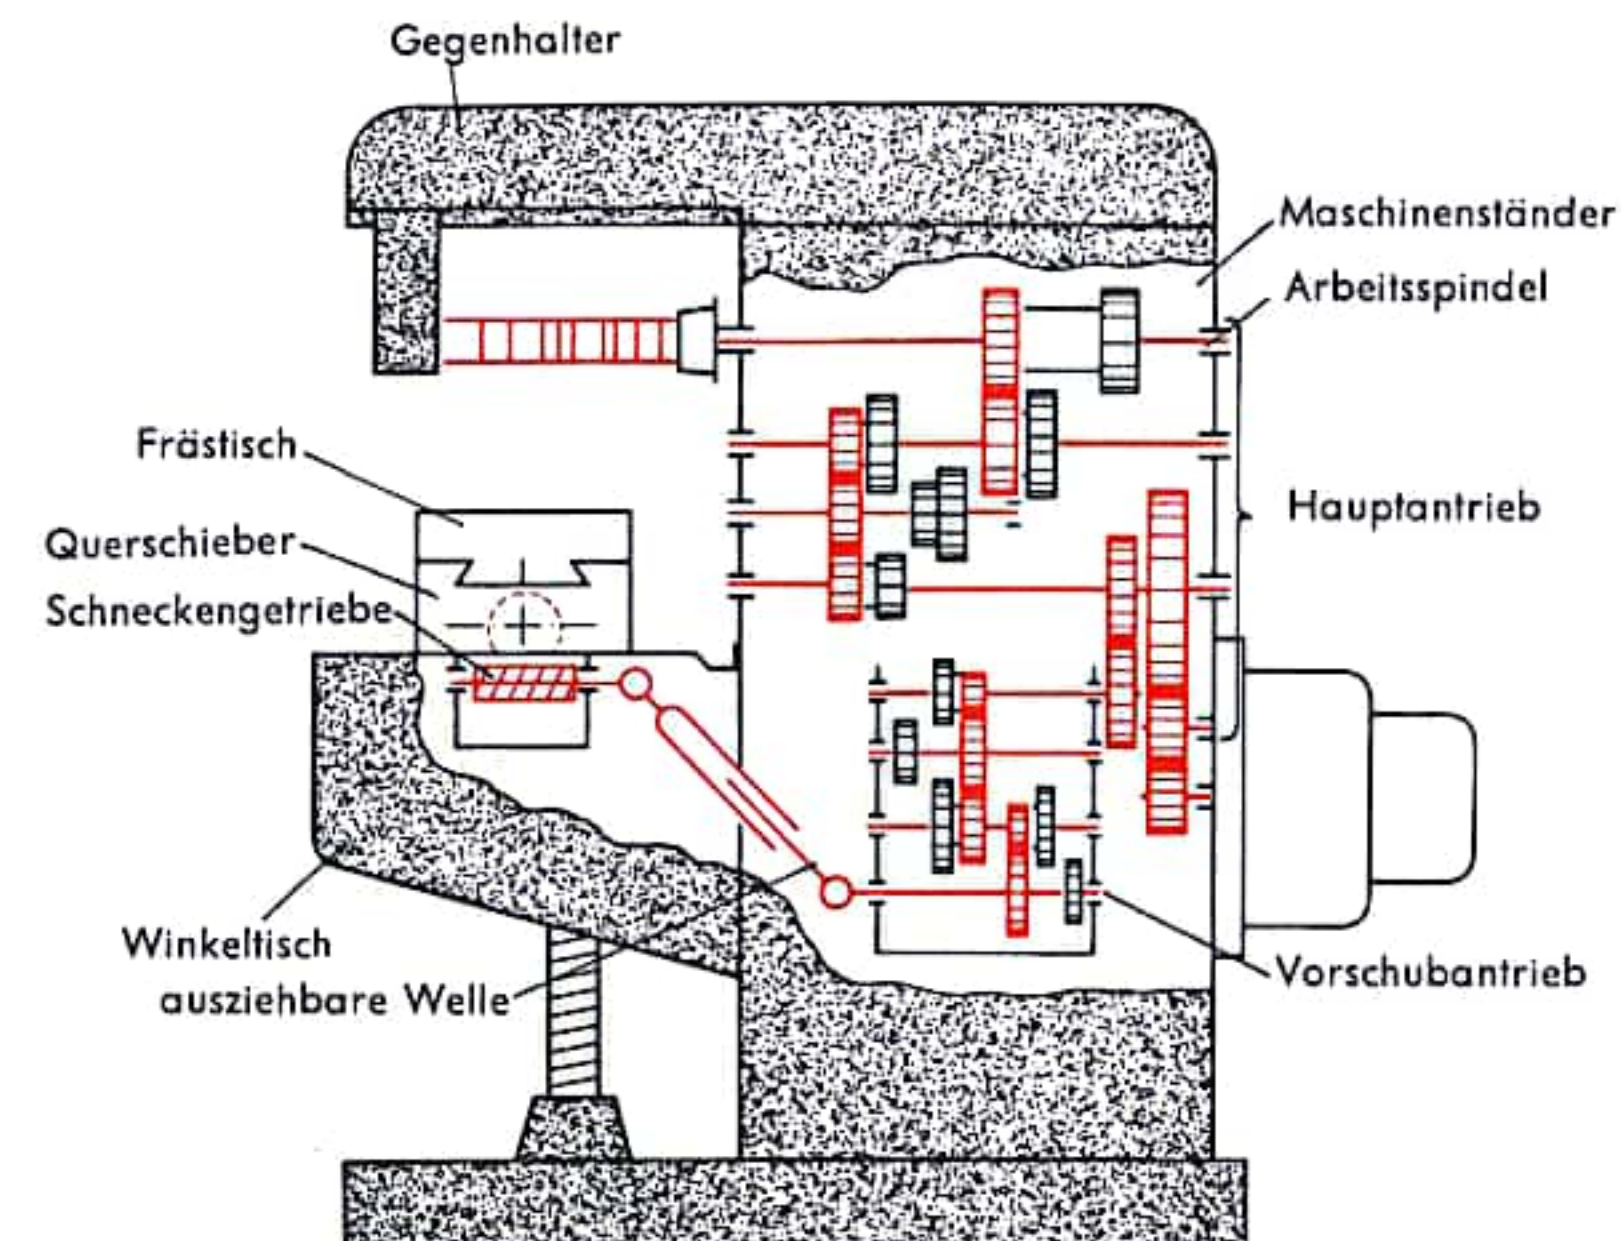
Hauptteile einer Waagrechtfräsmaschine
